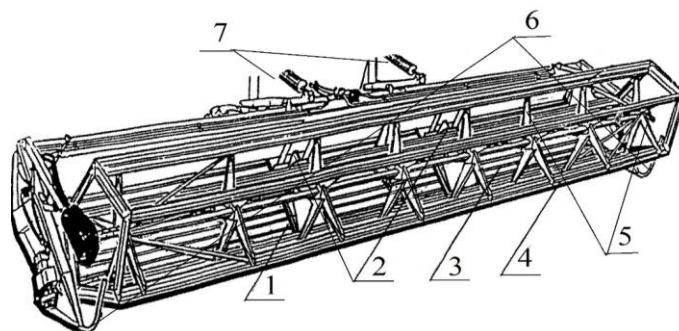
Порционная жатка: 1-рама жатки; 2-устройства отвода хлебной массы от колес; 3- транспортер; 4- режущий аппарат; 5- мотовило; 6-башмаки; 7-навеска
